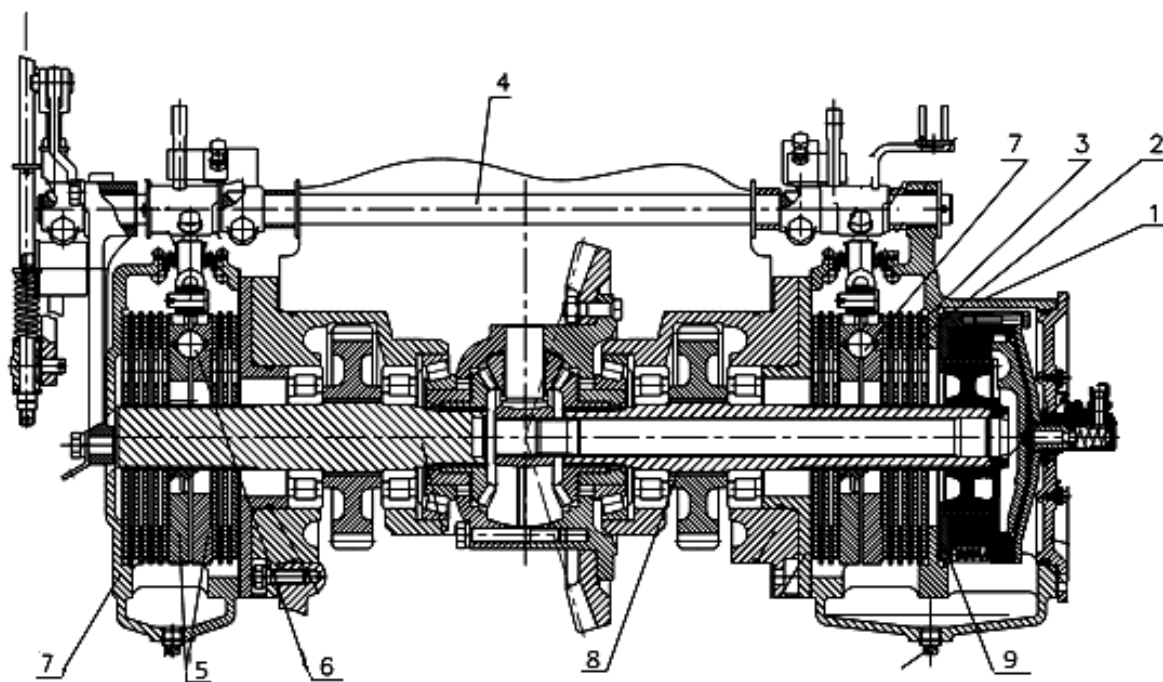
Рабочие тормоза трактора «Беларус-1523»: 1 – корпус тормоза; 2 – диск фрикционный; 3 – диск промежуточный; 4 – валик педалей; 5 – диск нажимной; 6 – шарик; 7 – корпус тормоза; 8 – ведущая шестерня конечной передачи; 9 – муфта блокировки дифференциала
